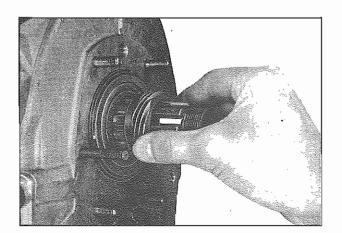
Montaggio della vite senza fine Fiting the tachometer worm
